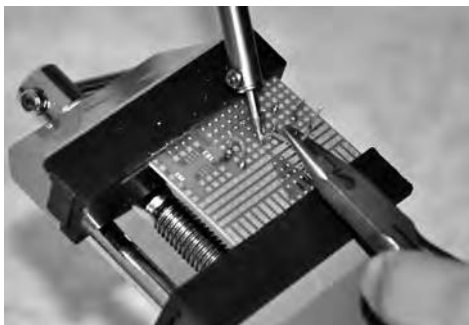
Anche con questa variante è facile tirare il filo durante il riscaldamento.
